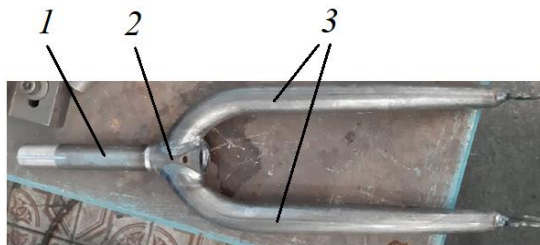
Рулевая вилка: 1 – стержень; 2 – коронка; 3 – перья
